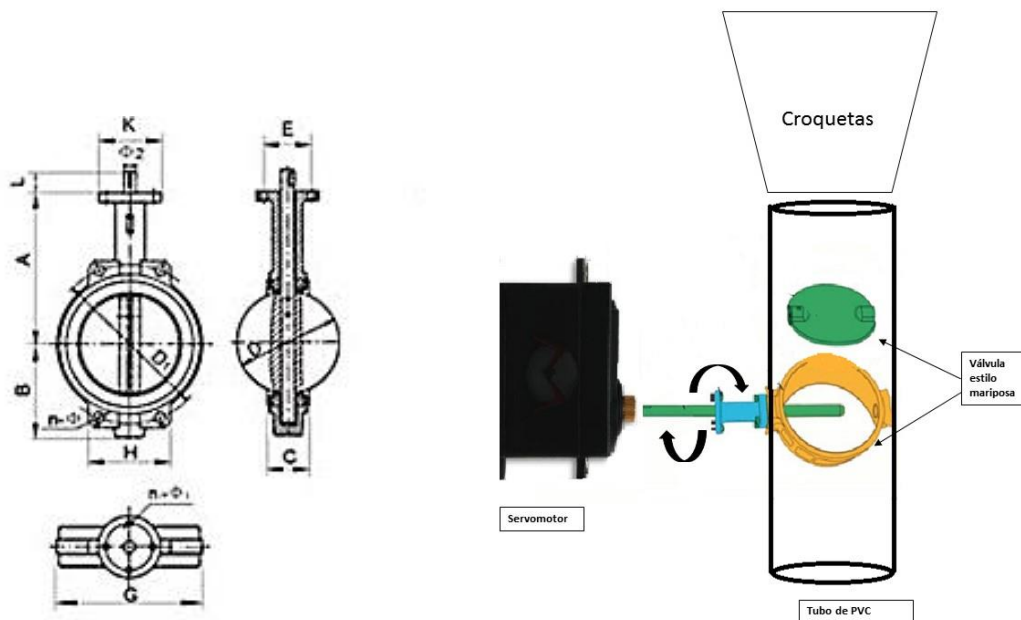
Diseño del dispensador de croquetas. [21] [22]
